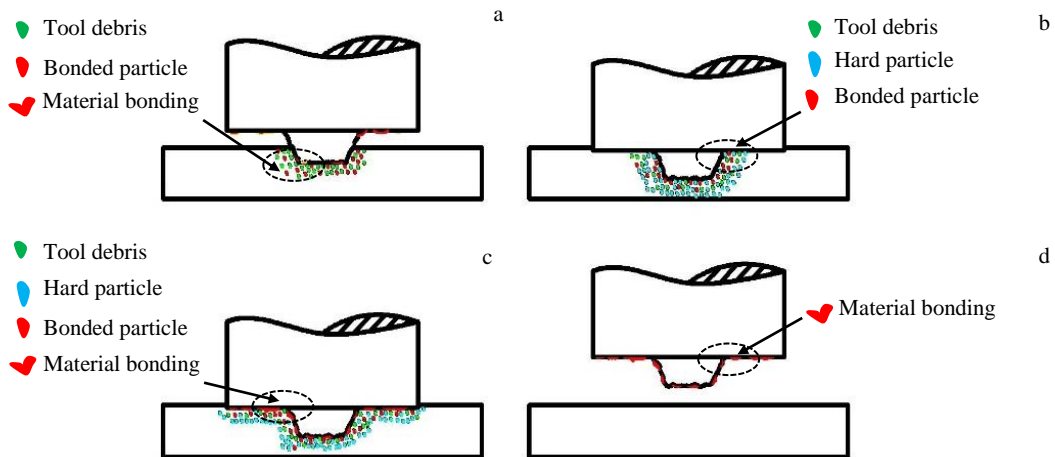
使用后的搅拌头焊接磨损原理示意图
